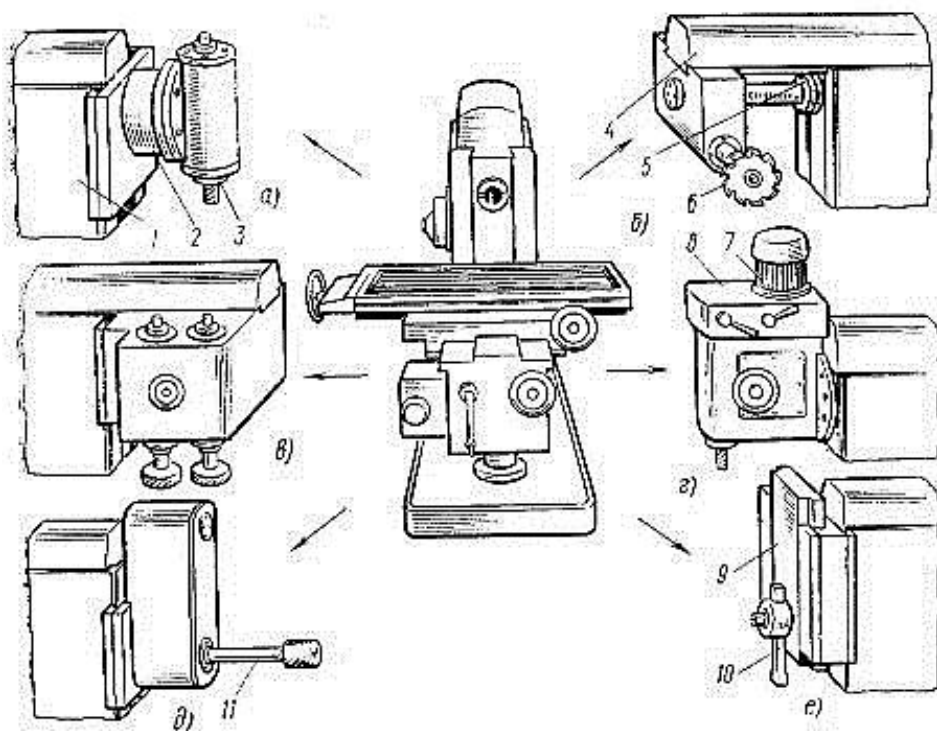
Спеціальні пристосування, що розширюють технологічні можливості фрезерних верстатів: а – додаткова вертикально-фрезерна головка; б – пристосування для фрезерування рейок; в – двошпиндельна фрезерна головка; г - свердлильна головка; д – шліфувальна головка; е – довбальна головка.
